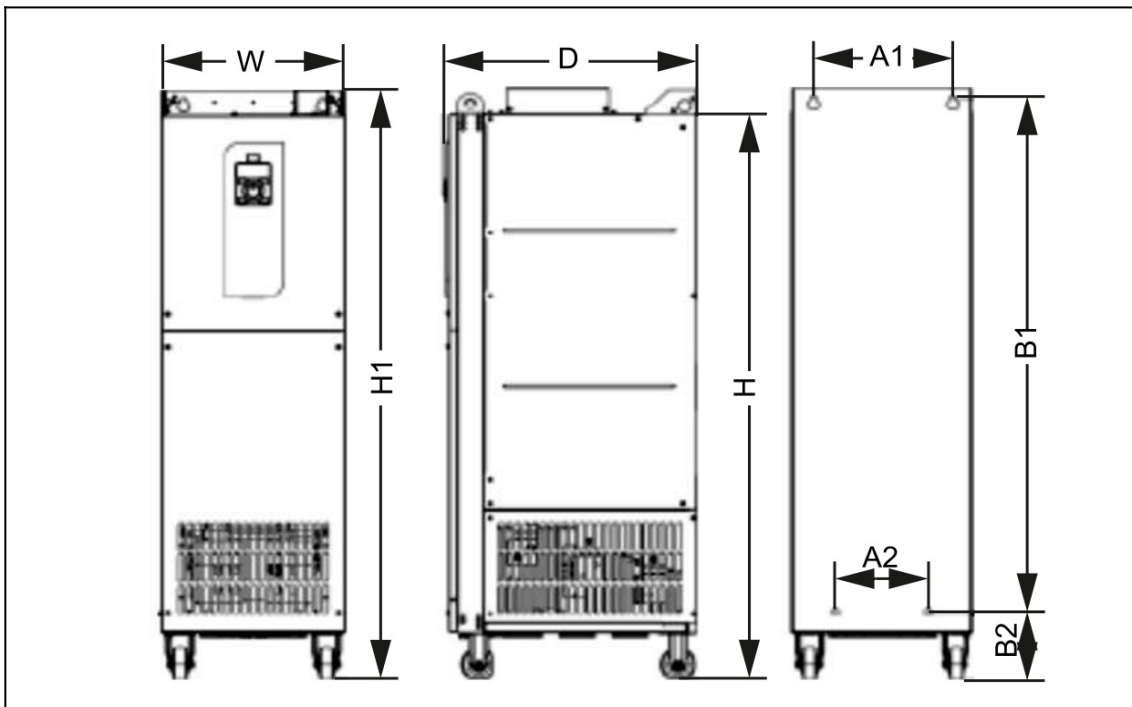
Размеры корпусов Т8-Т10 без дополнительного основания
